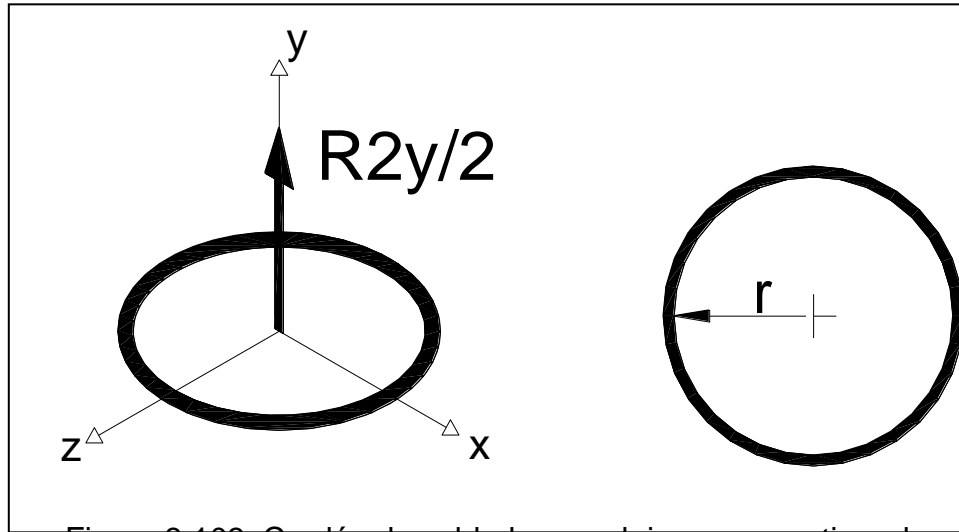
Cordón de soldadura anclaje sup. amortiguador
